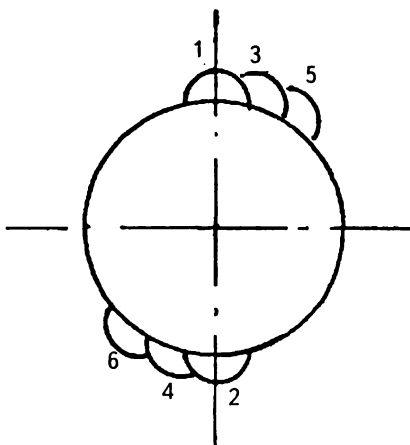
Порядок наложения швов при наплавке деталей цилиндрической формы
